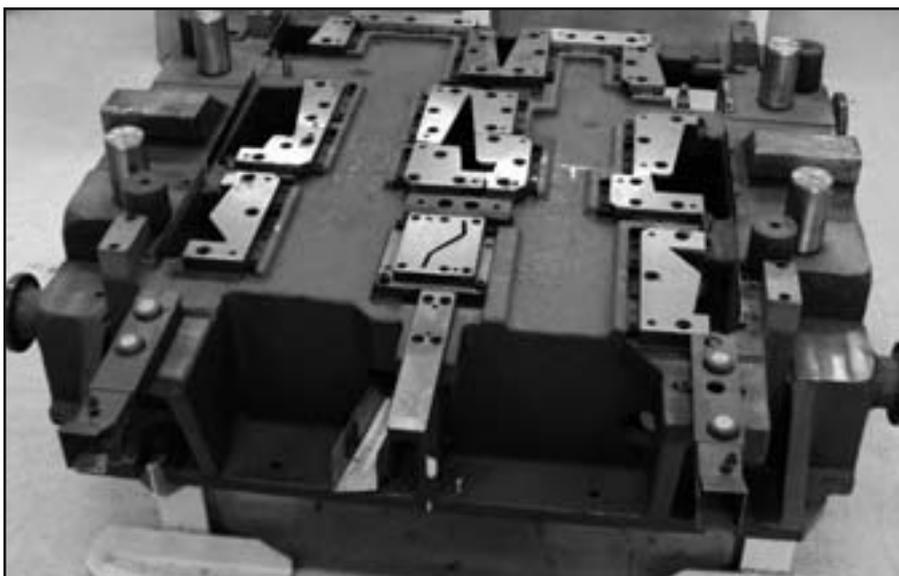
Beispiel eines „Trainingswerkzeuges“ (Unterteil eines Großschneidwerkzeugs aus der Automobilindustrie)
